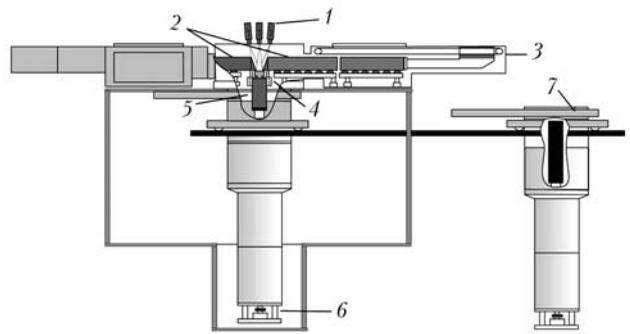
Схема установки ВТ01: 1 — пушка ВТР; 2 — переплавляемая заготовка; 3 — механизм подачи заготовки; 4 — водоохлаждаемый кристаллизатор; 5 — слиток; 6 — механизм вытягивания; 7 — вакуумный затвор
